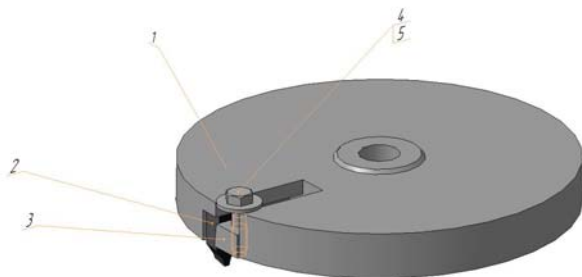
Торцева різцева головка з регульованим розташуванням різця
